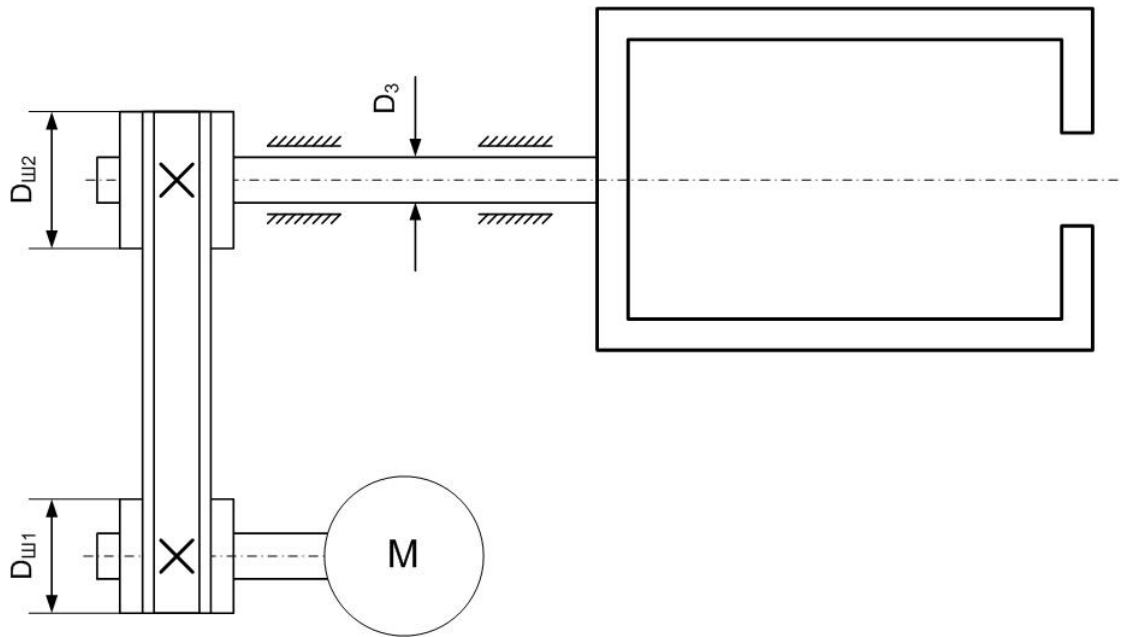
Кінематична схема установки відцентрового лиття
